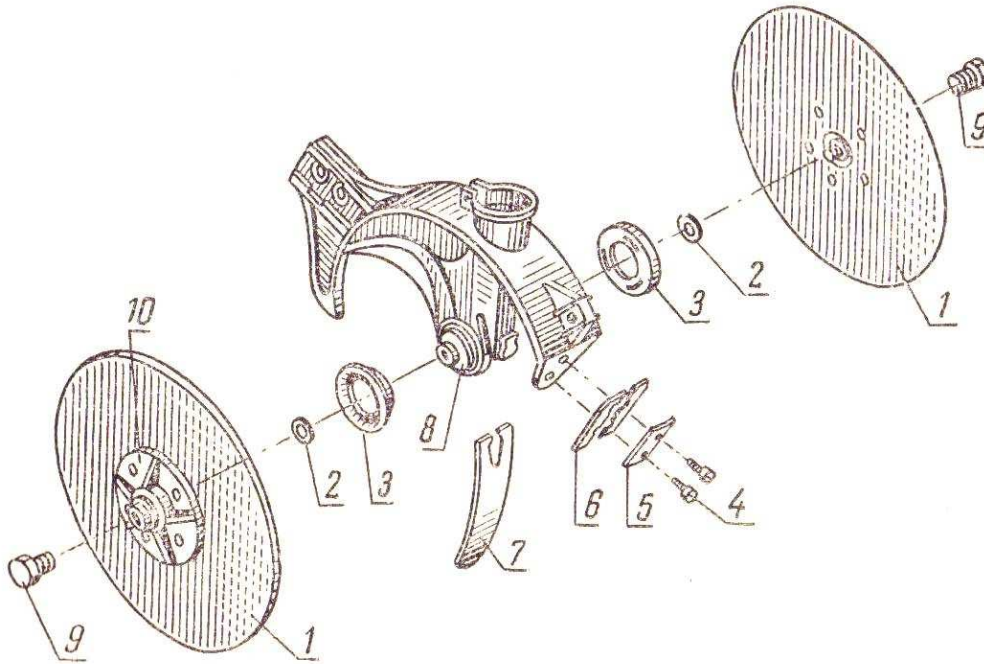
Задний дисковый сошник: 1 – диск; 2 – шайба; 3 – уплотнитель; 4 – болт; 5 – прижим; 6 – чистик; 7 – направитель; 8 – корпус; 9 – пробка; 10 – крышка
